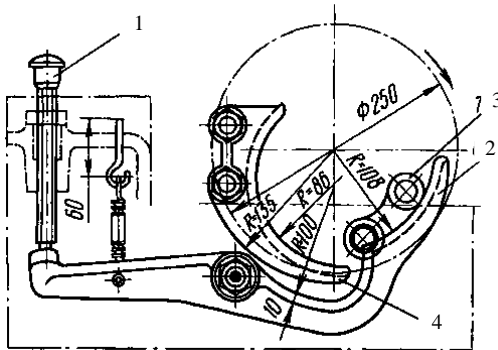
Регулятор маси заготовок РМК-60: 1 – гвинт; 2 – рухома напрямна; 3 – ролик; 4 – валок
